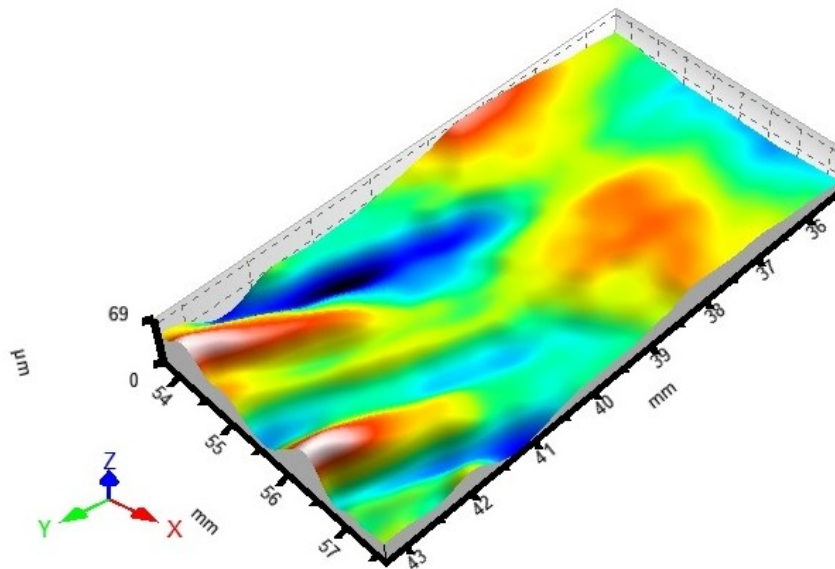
reálný 3D pohled snímaného povrchu vzorku Q1
